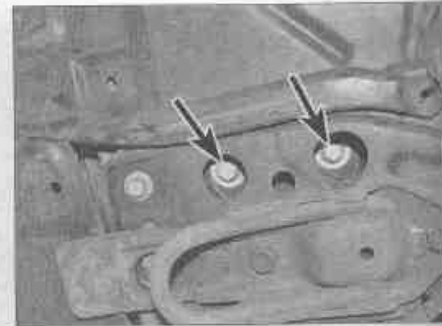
Нижние болты крепления передней опоры двигателя
